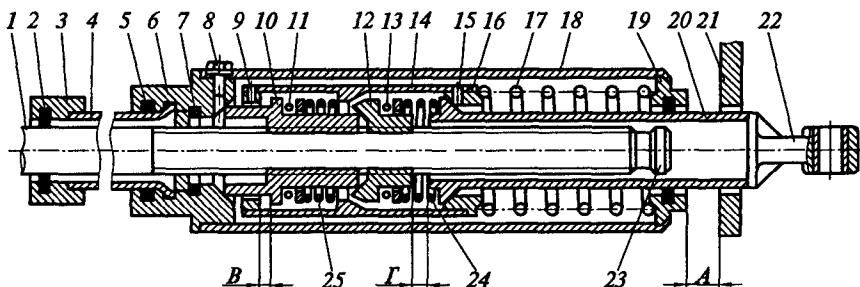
Механизм авторегулятора тормозной рычажной передачи усл. № 574Б в исходном положении:
